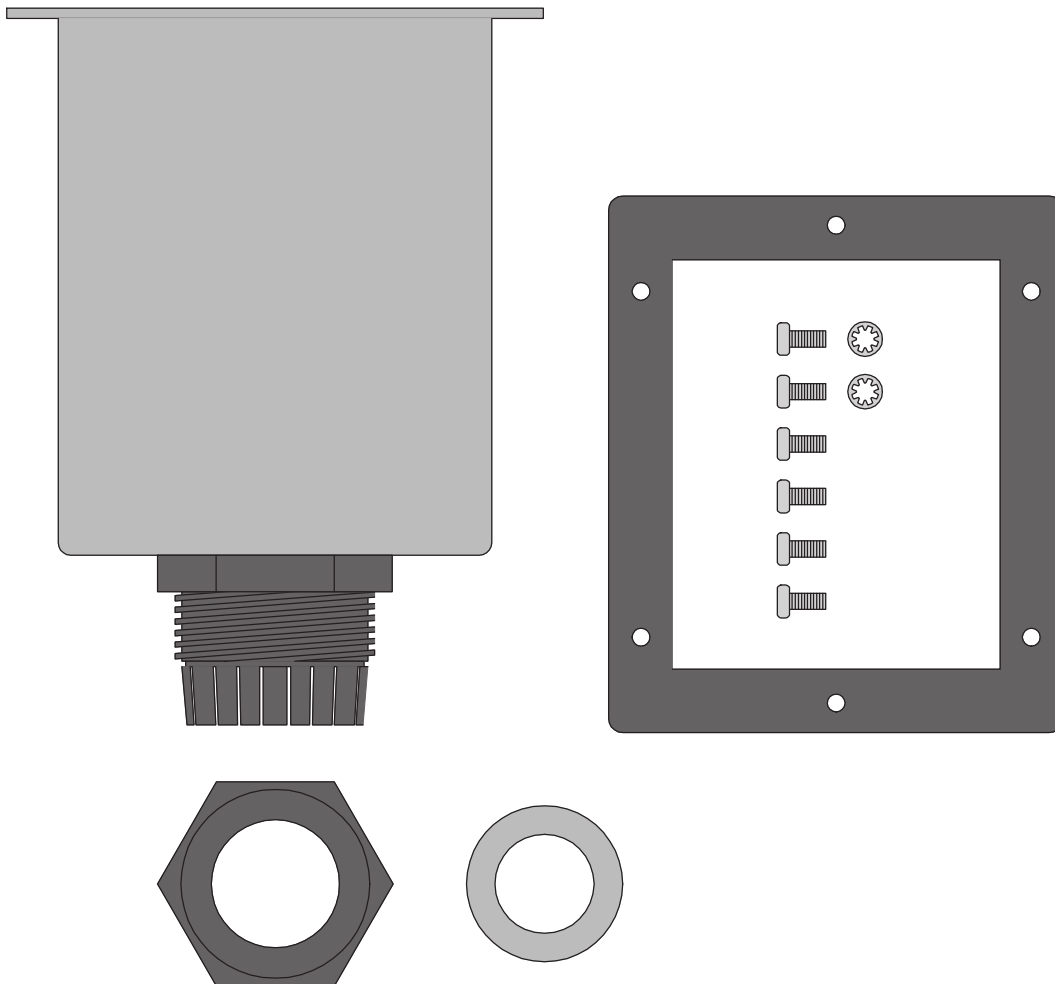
Lieferumfang AC-Anschlussgehäuse mit metrischer Verschraubung, Dichtungen, Befestigungsschrauben und Zahnscheiben
